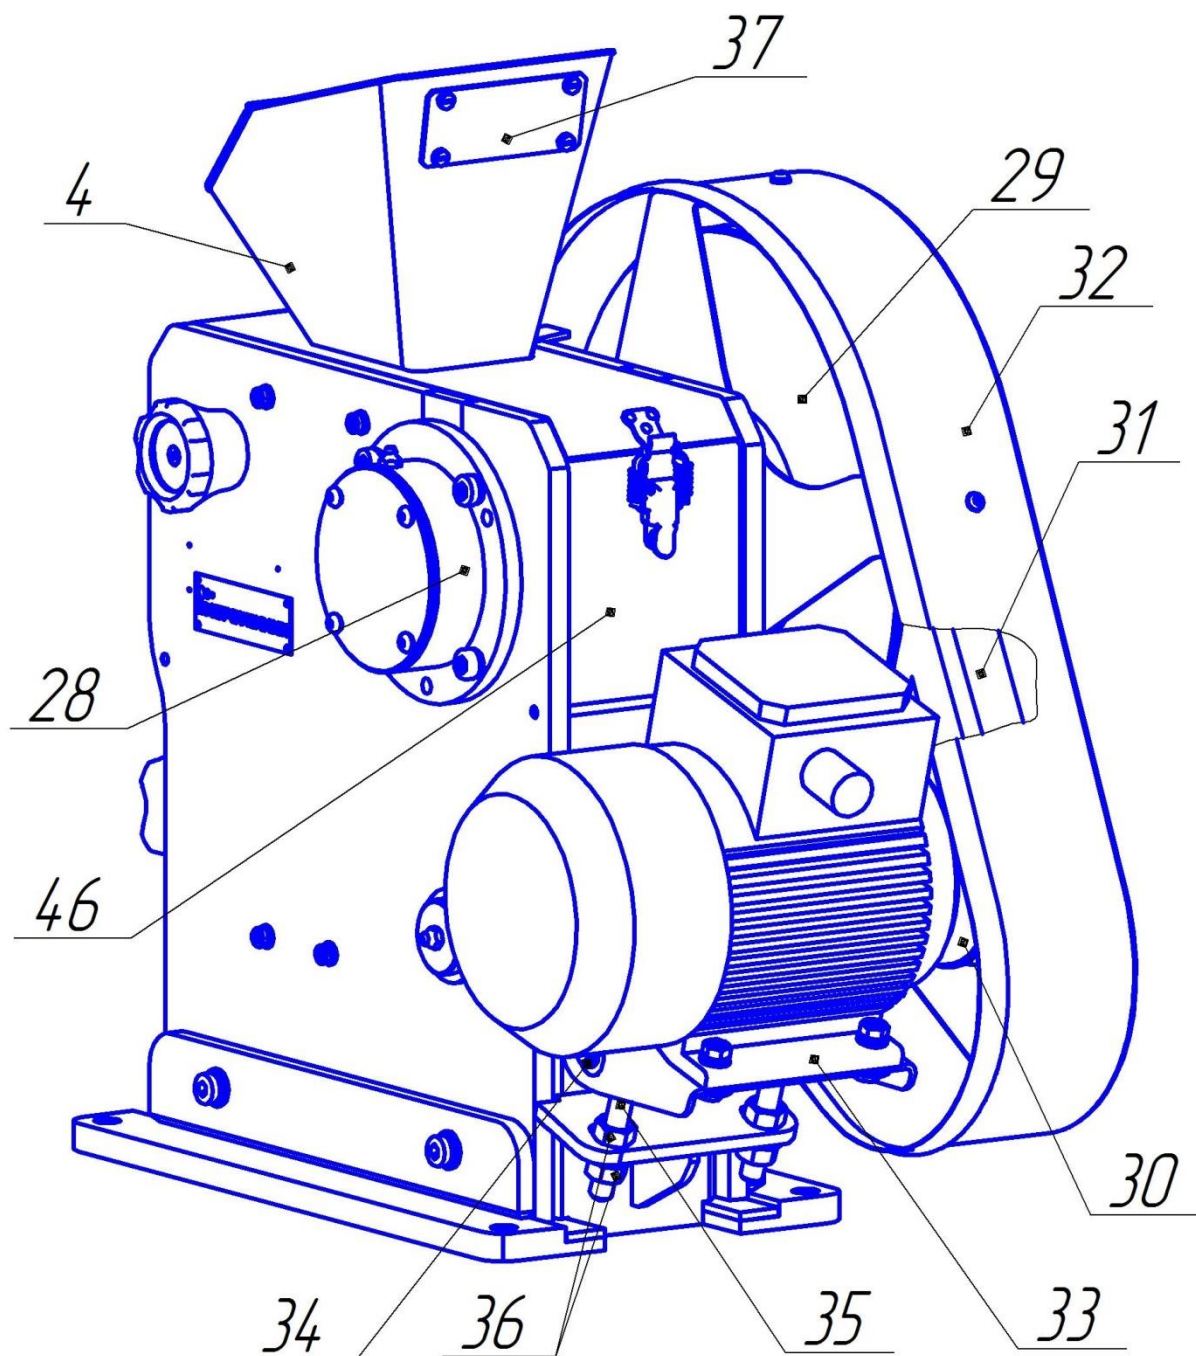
Б Общий вид дробилки ЩД 6М (продолжение)
